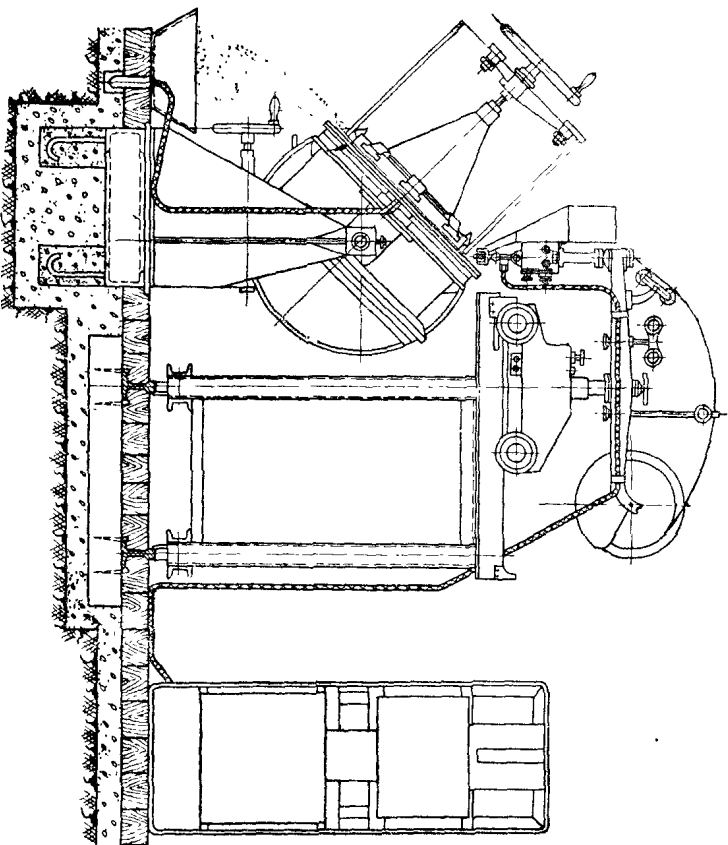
Установка для сварки продольных швов огневой коробки локомотива.
